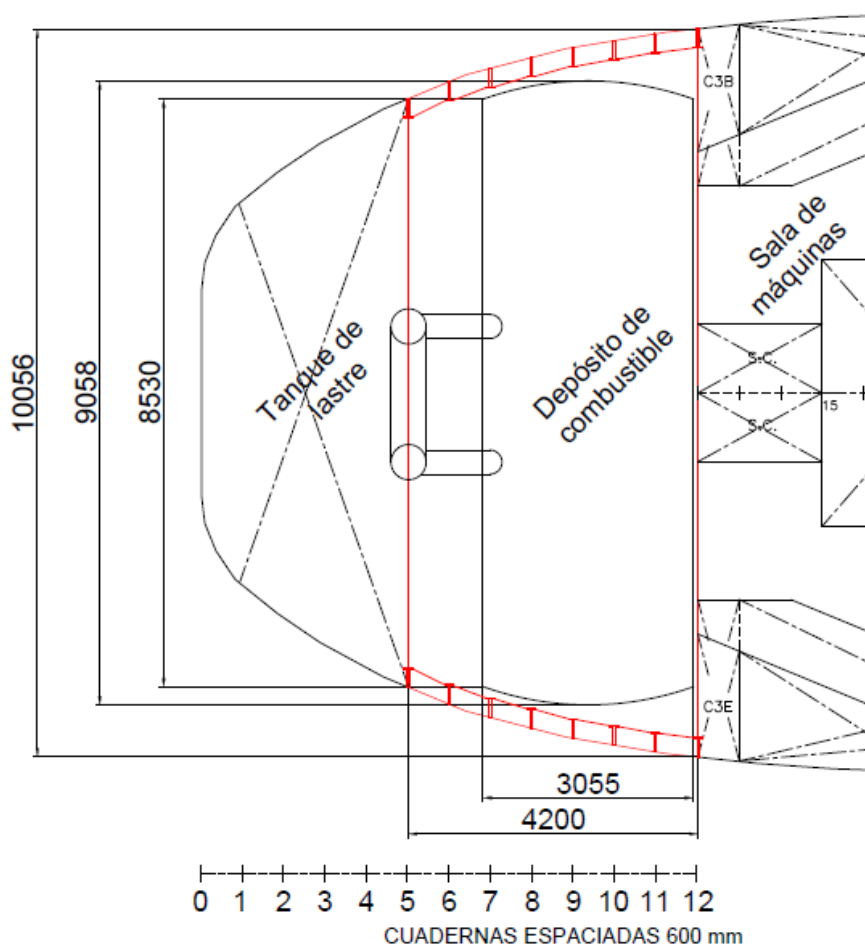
Disposición de la zona de popa vista de planta (distancias en mm)
